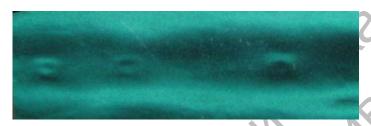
Индикаторный рисунок шлаковых включений в образце
